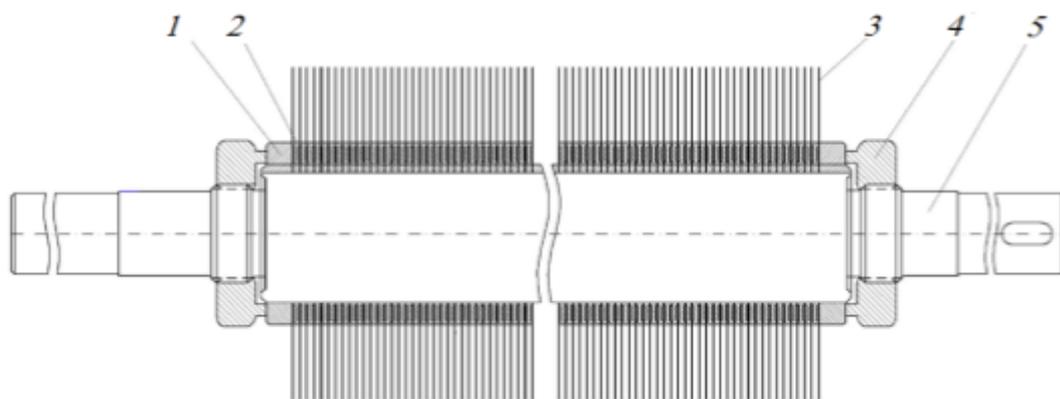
Пильный цилиндр пильного джина марки 4ДП-130
